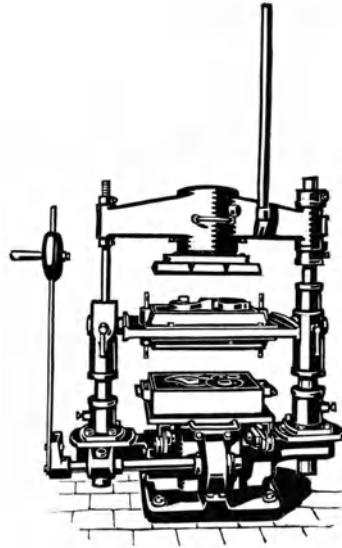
Wendplatten-Formmaschine mit Handpressung.
